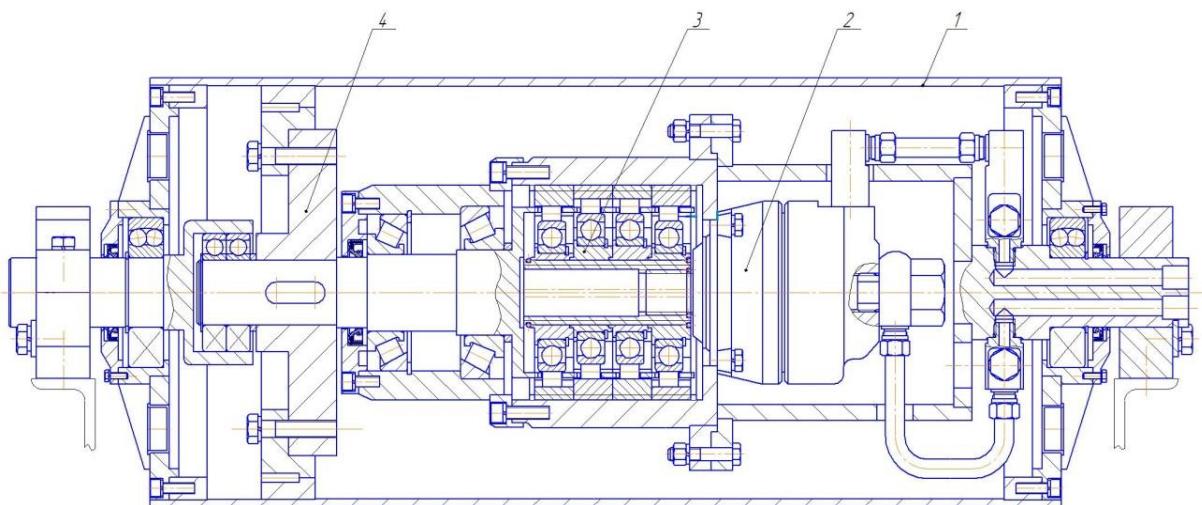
Конструкція гідравлічного вмонтованого привода з кульковою хвильовою передачею
